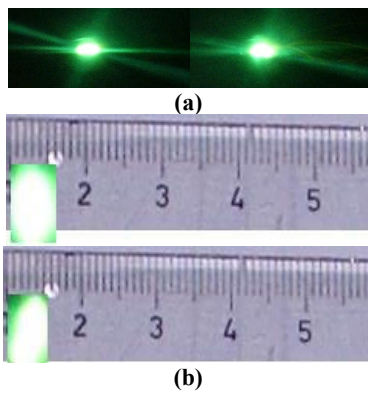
(a) Fotografías tomadas durante la elaboración del cordón de soldadura
